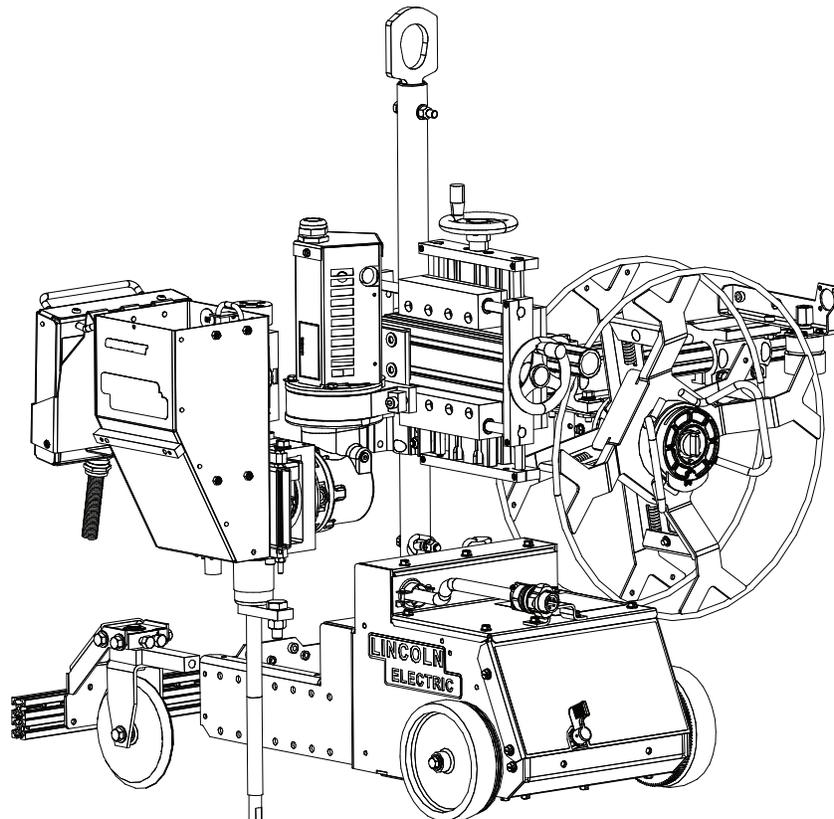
VISTA TRASEIRA SOLDAGEM DE TUBO
